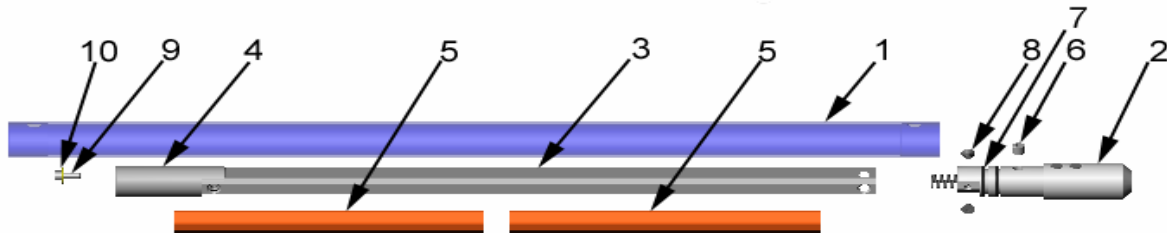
Outil de coupe Split Shot Cutter avec rails - Vue éclatée
